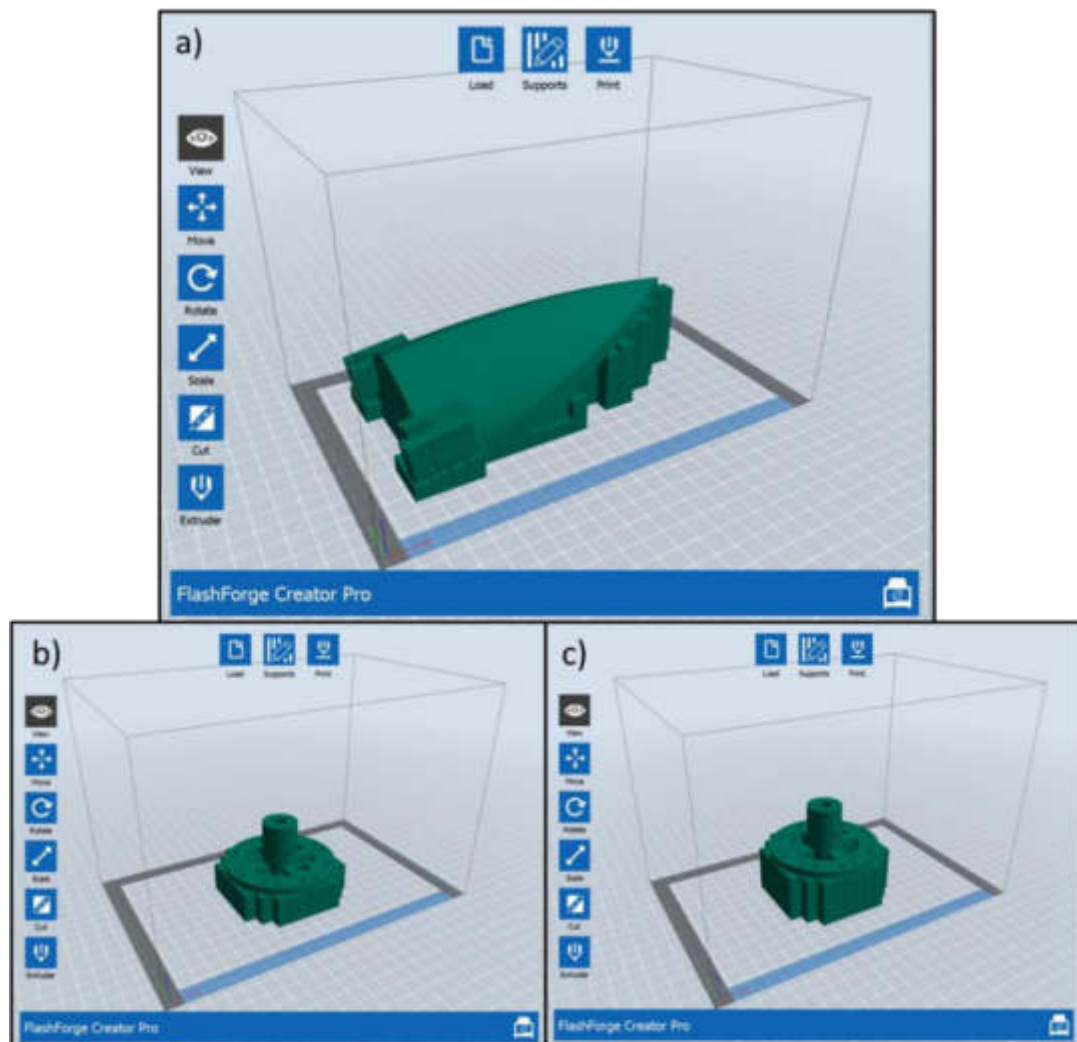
Visualización de la impresión de los elementos de la turbina: a) Álabes, b) Rotor Inferior y, c) Rotor superior.
